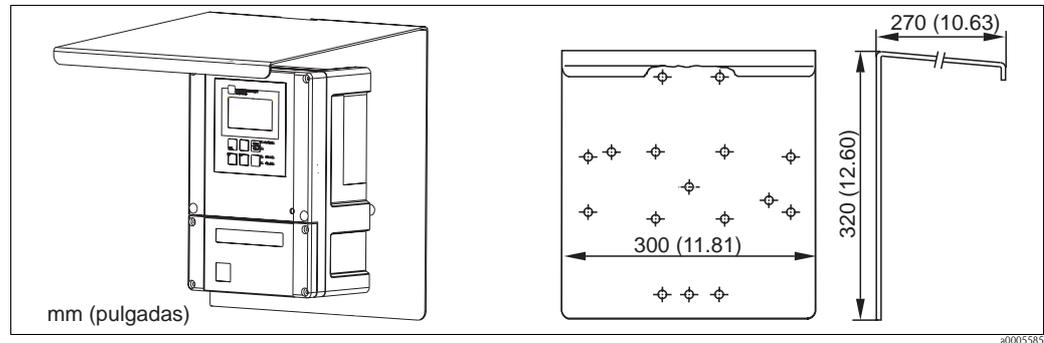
Cubierta de protección contra intemperie para el instrumento de campo)
